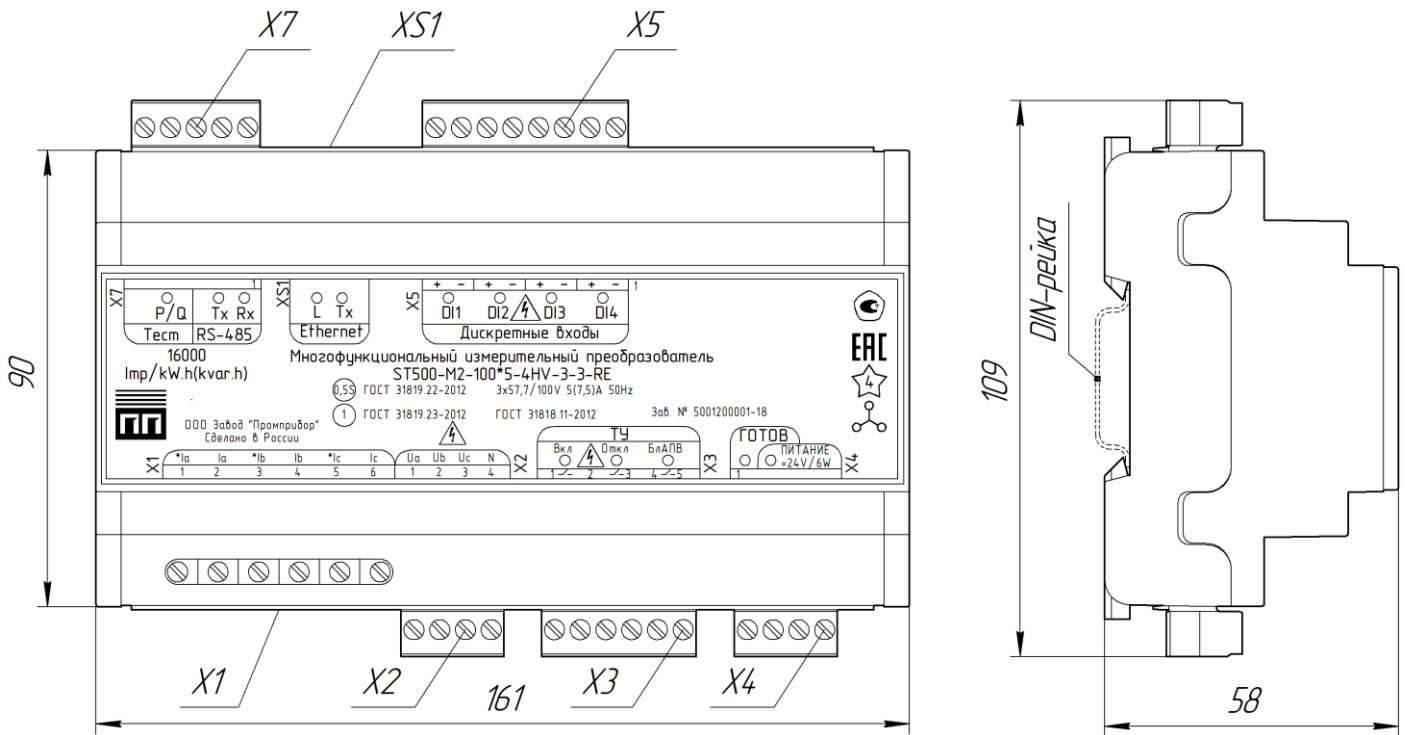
Внешний вид и габаритные размеры МИП ST500-M2-XXX*X-4HV-3-3-RE и ST500-M2.02-XXX*X-4HV-3-3-RE
